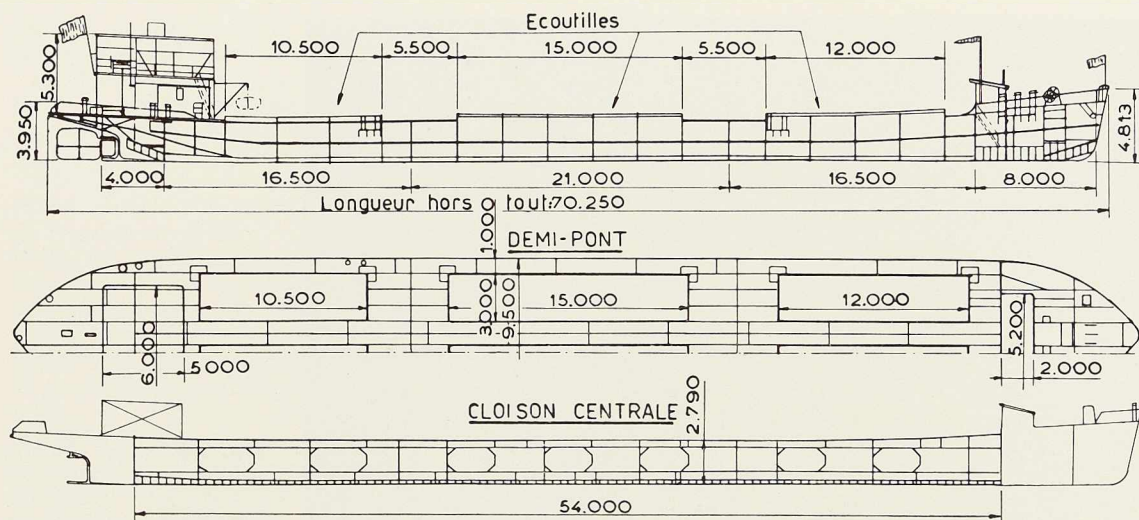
Détails constructifs d'une barge naviguant sur le fleuve Congo.
